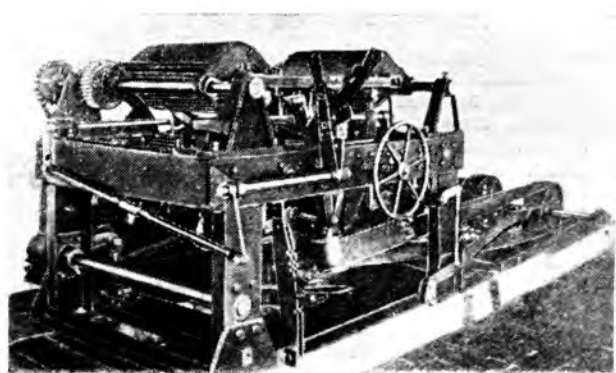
Двухшпиндельный шпалооправочный станок ШОСД-5
